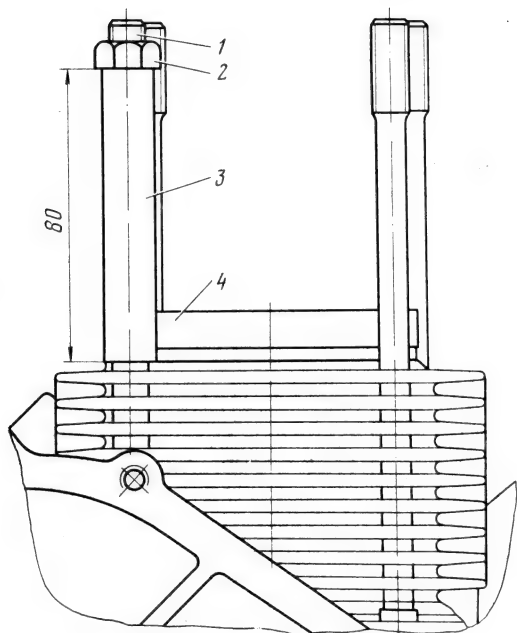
Крепление цилиндров на картере коленчатого вала:
